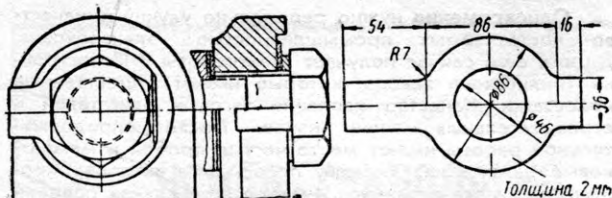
Стопорная шайба болта кожуха зубчатой передачи
